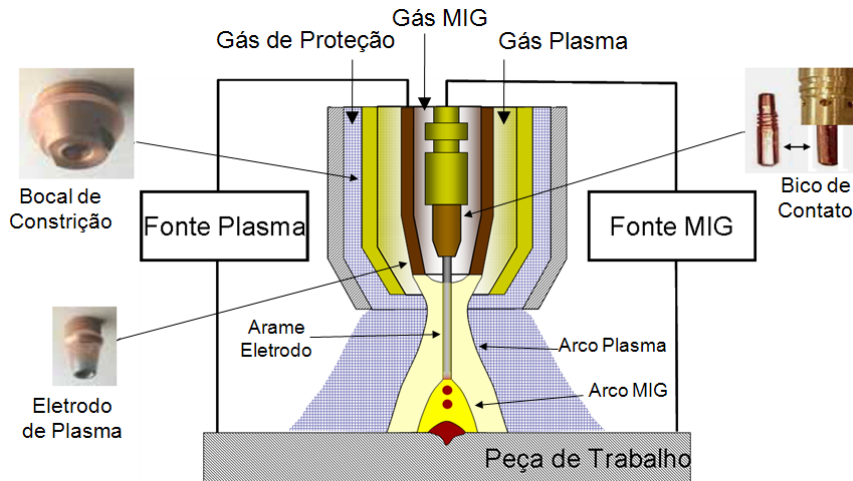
Desenho esquemático de uma tocha para soldagem Plasma-MIG, com destaque para os componentes principais (Adaptado de Oliveira, 2006).
